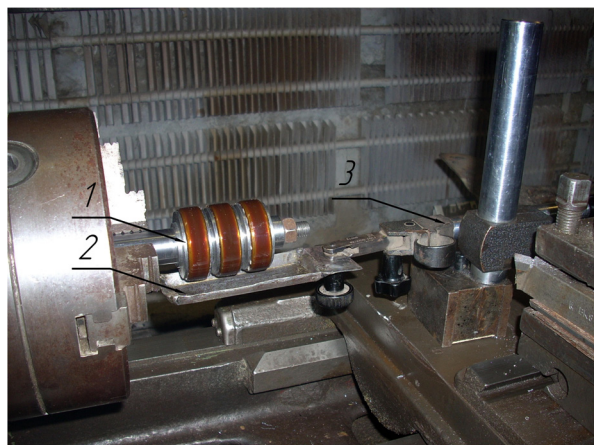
Лабораторная установка для нанесения полимерных покрытий
